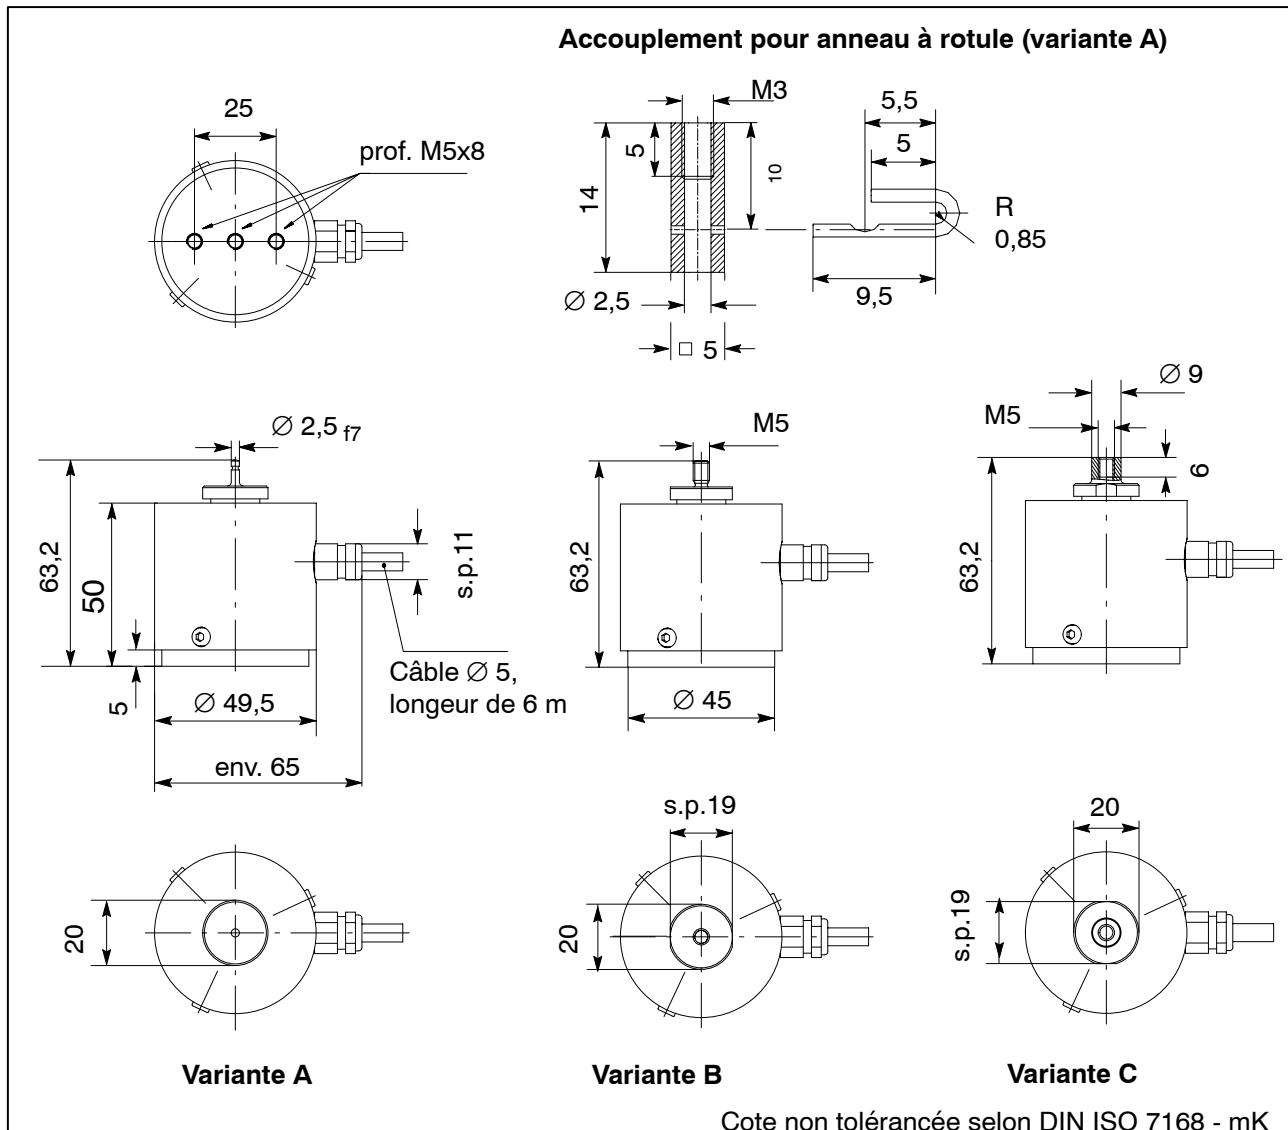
Dimensions du capteur U1A et des anneaux à rotule
